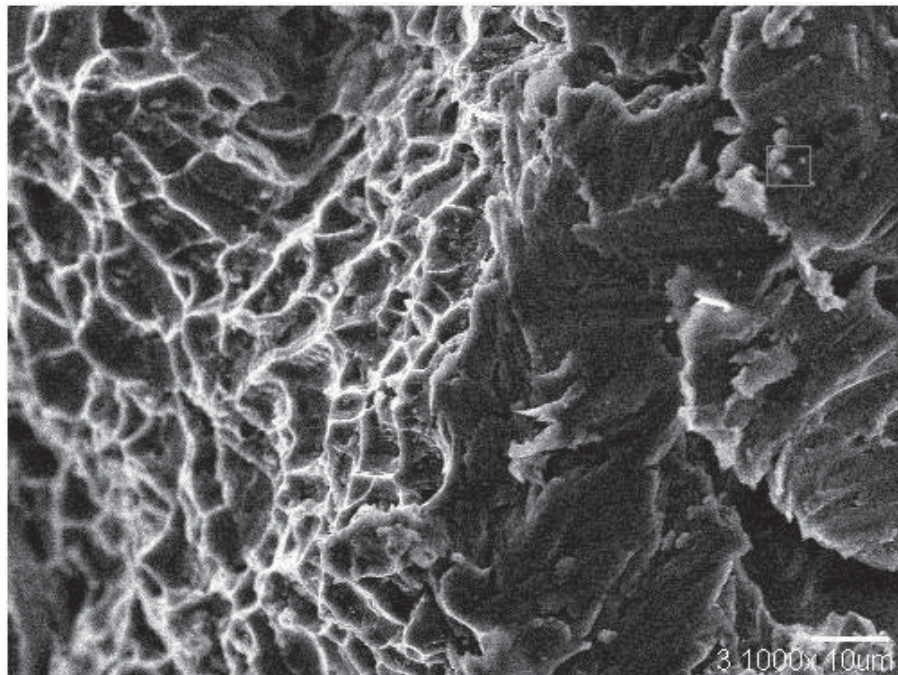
Microanálisis de la superficie de fractura de las soldaduras
